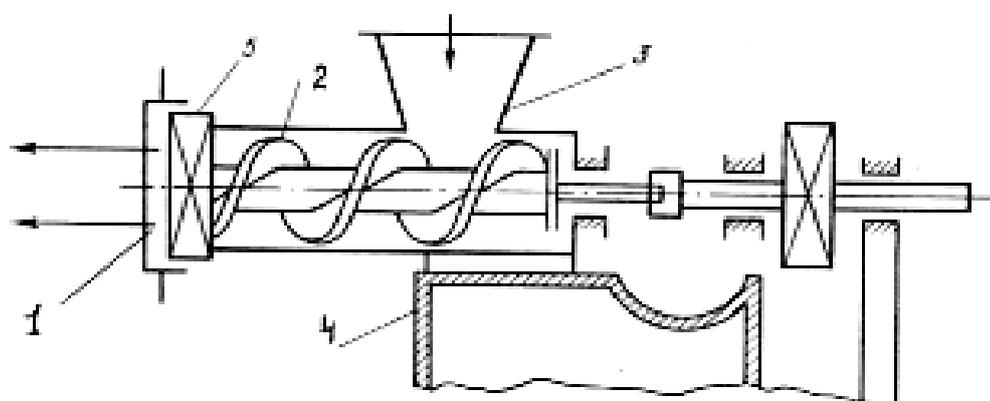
Волчок: 1 – решетка; 2 – шнек; 3 – загрузочная воронка; 4 – станина; 5 – режущий механизм
